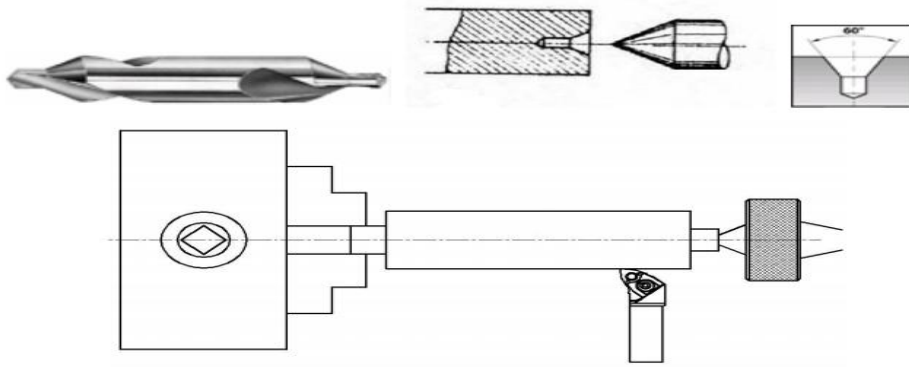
Pieza montada en plato de tres mordazas con punto³⁷.
